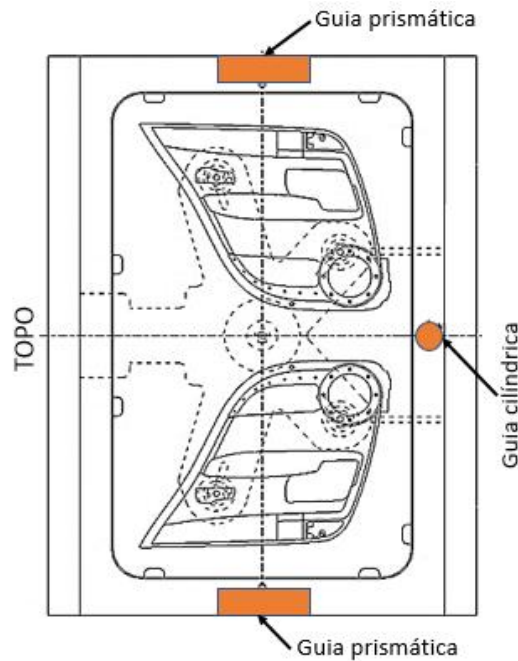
Molde com guias prismáticas (Grupo Simoldes, 2016)
